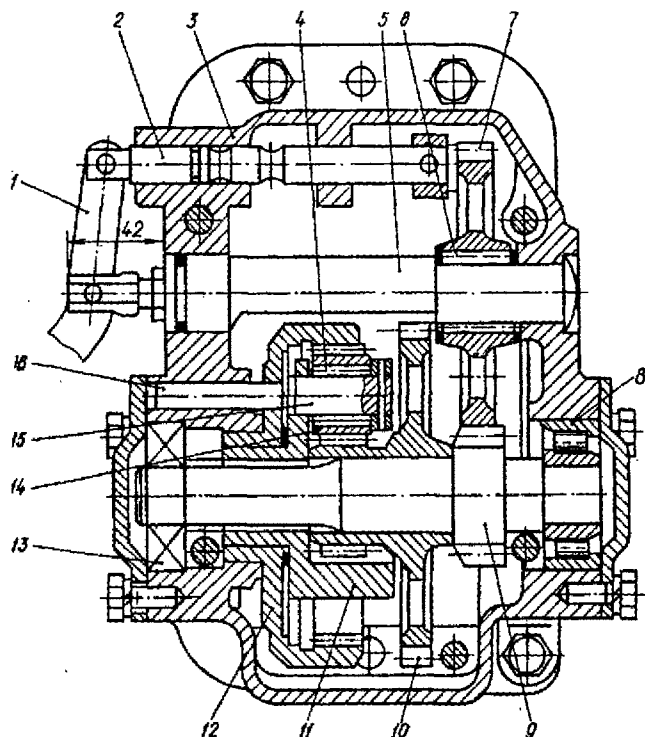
Ходоуменьшитель тракторов семейства МТЗ: 1 - рычаг; 2 - вал; 3 - корпус; 4 - игольчатый подшипник; 5 - ось; 6, 8 и 13 - подшипники; 7 - промежуточная шестерня; 9 - вал-шестерня; 10 - двойная шестерня; 11 - водило; 12 - коронная шестерня; 14 - сателлит; 15 - ось сателлита; 16 - палец
